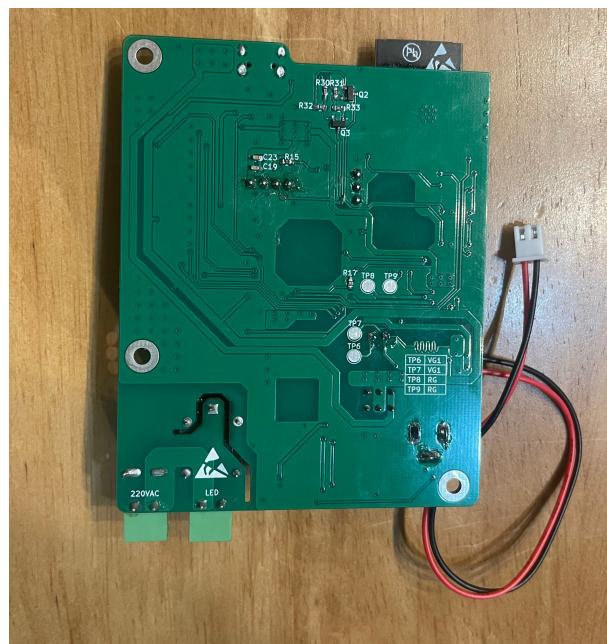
Hình ảnh thiết kế mặt dưới của PCB
